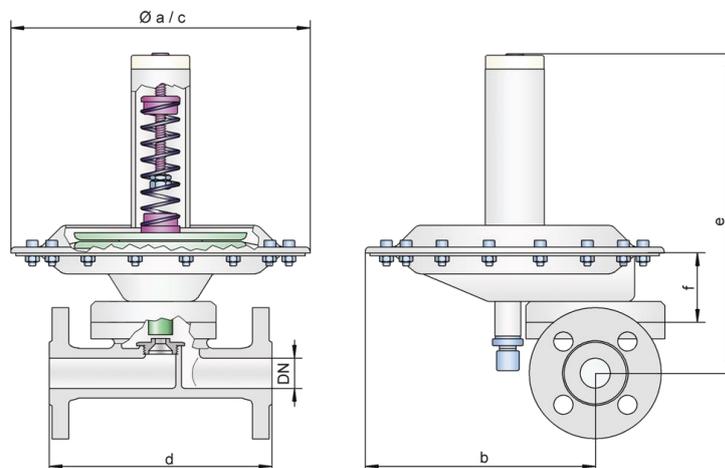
Válvula Blanketing. Fuente: <https://www.protego.com/es/productos/detail/ZM-R.html>
